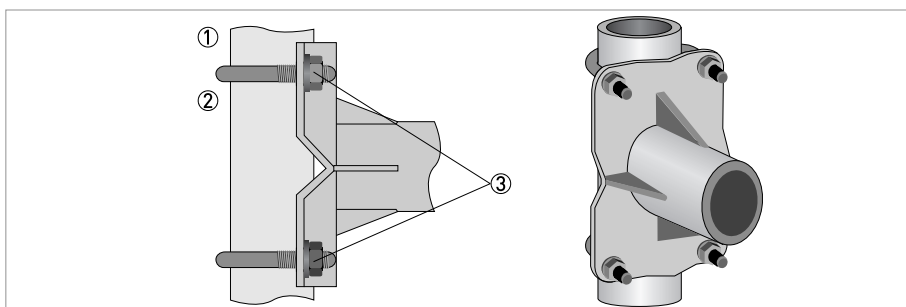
Крепление корпуса преобразователя сигналов полевого исполнения к трубе
